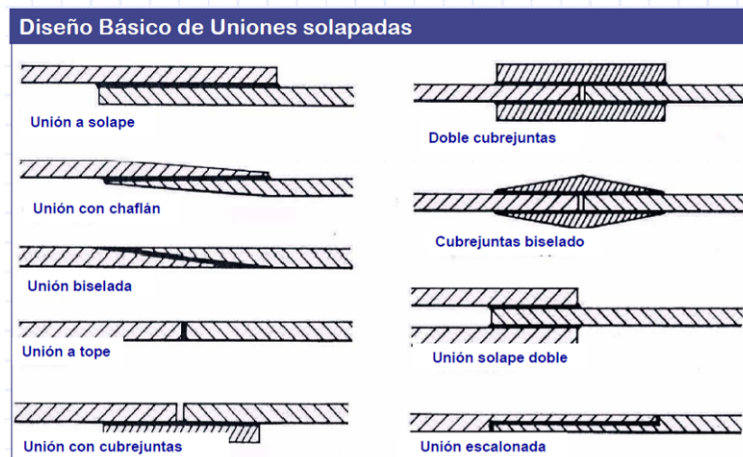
Diseños que reducen el efecto de las fuerzas excéntricas [26].
